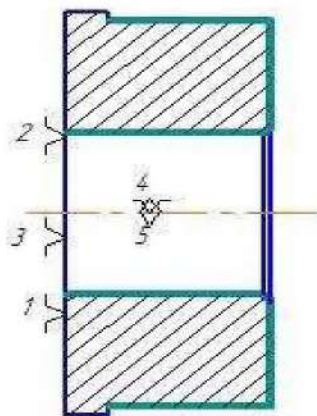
Схема базування заготовки на токарній операції 005.
